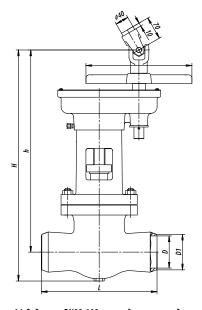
Задвижка DN80-100 с цилиндрическим редуктором
